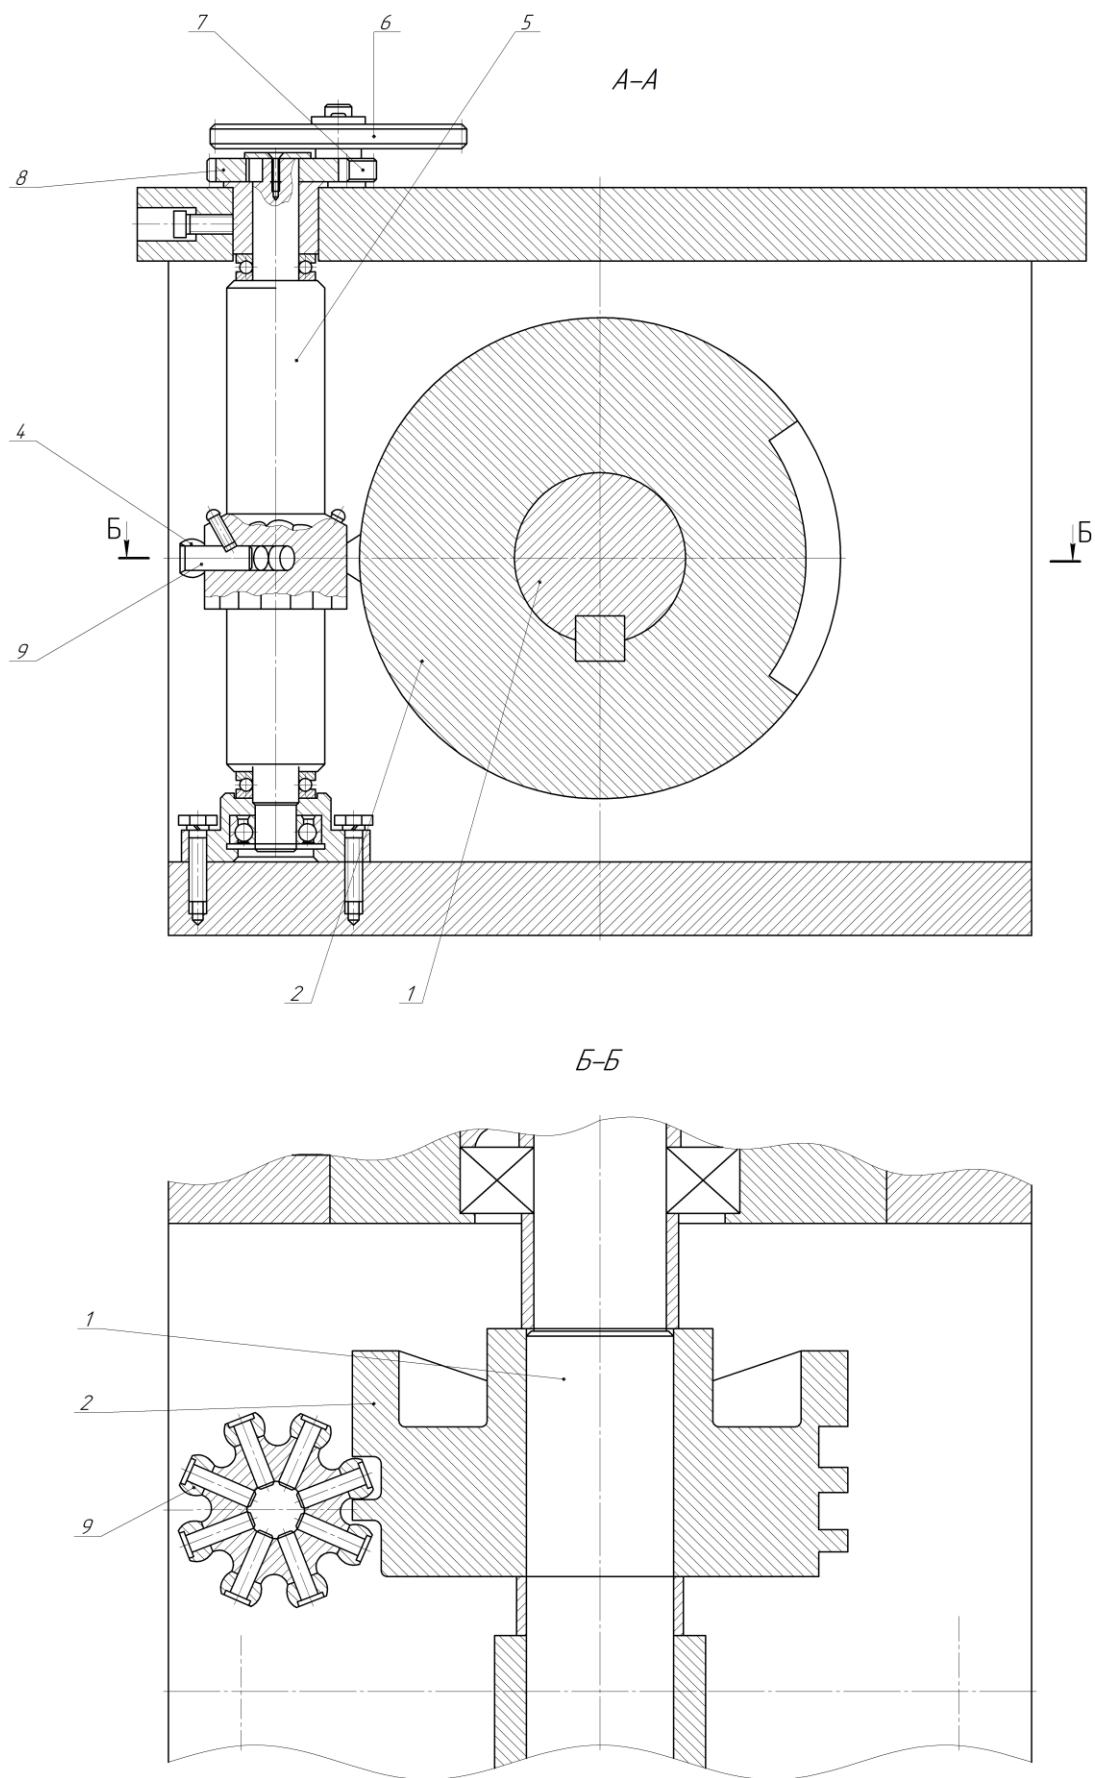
Нова конструкція приводу повороту ротора
